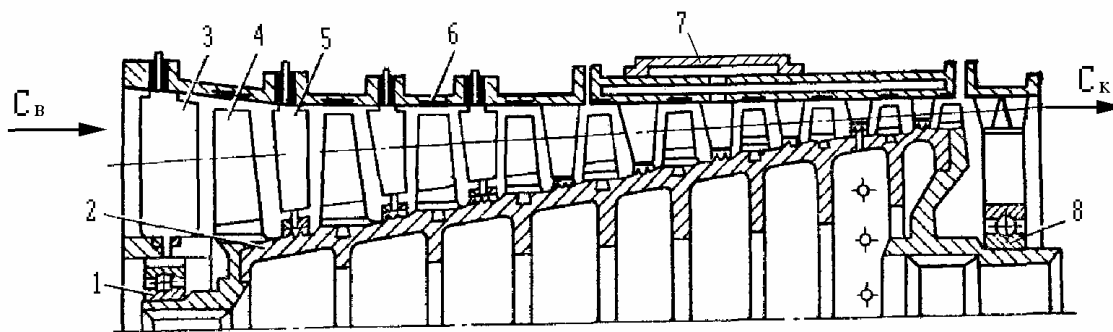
Схема устройства осевого компрессора ТВад*:
